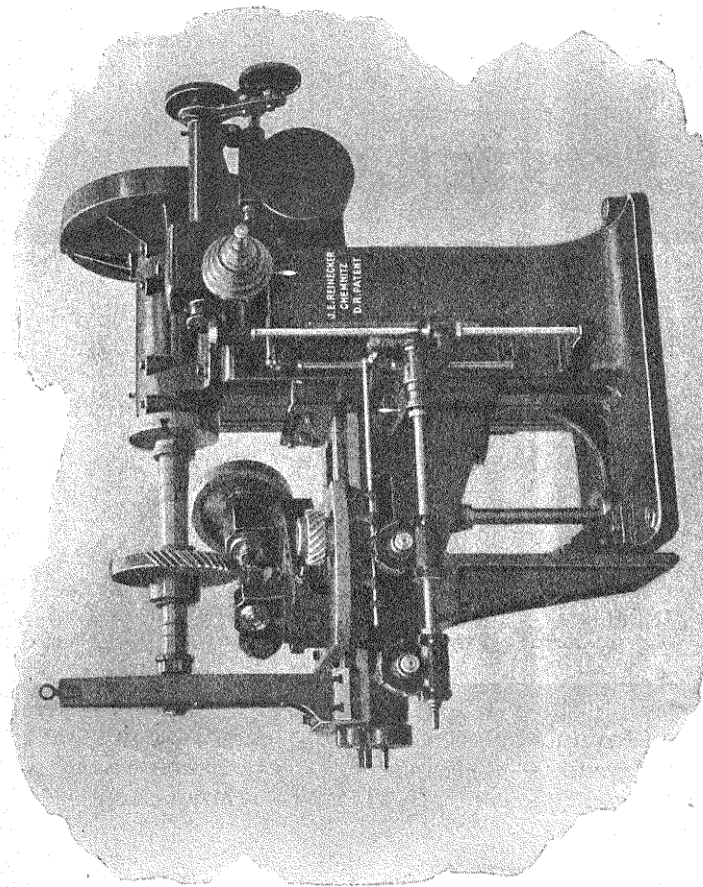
Machine universelle à fraiser les engrenages Reincker.
